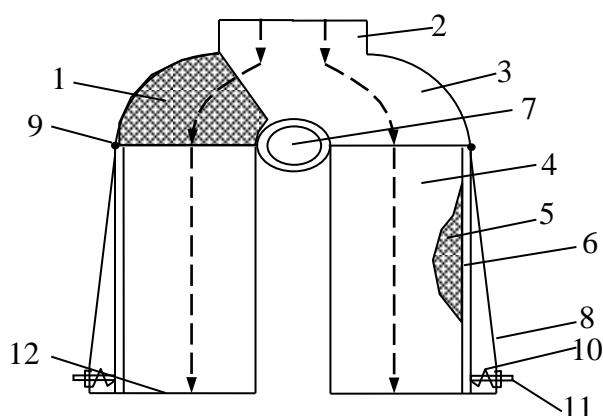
Установка електрохімічної обробки соломи : 1 - ущільнюючий орган;
